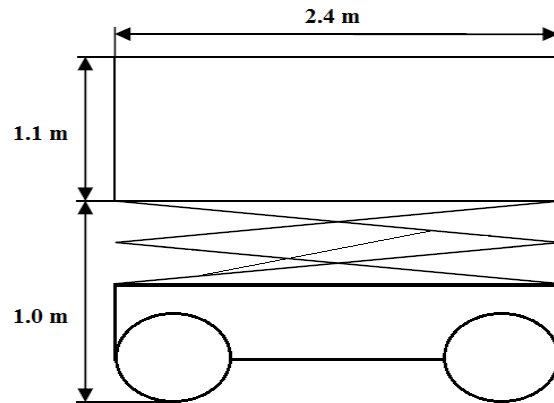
Elevadora en su posición con las tijeras plegadas.
